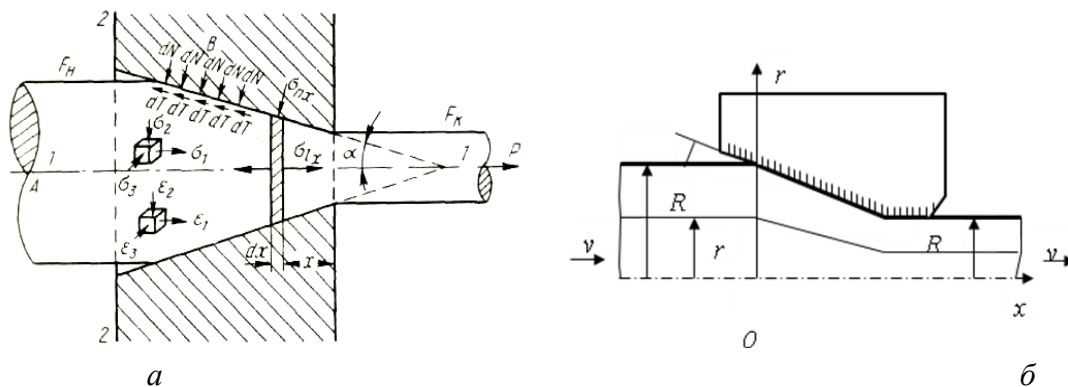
Процесс волочения прутковой заготовки через коническую матрицу – а; б – схема волочения.
